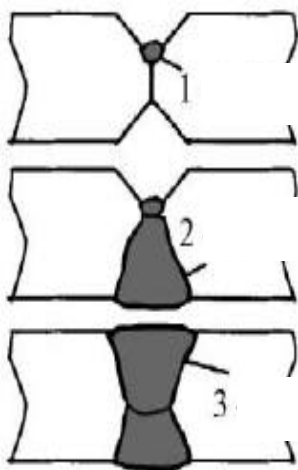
Aplicación de soldadura. 1) Punteo, 2) Soldadura interna y 3) Soldadura externa (Wen, 2001).
